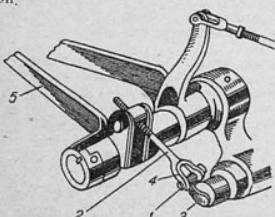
Привод механизма сцепления автомобиля ГАЗ-АА
